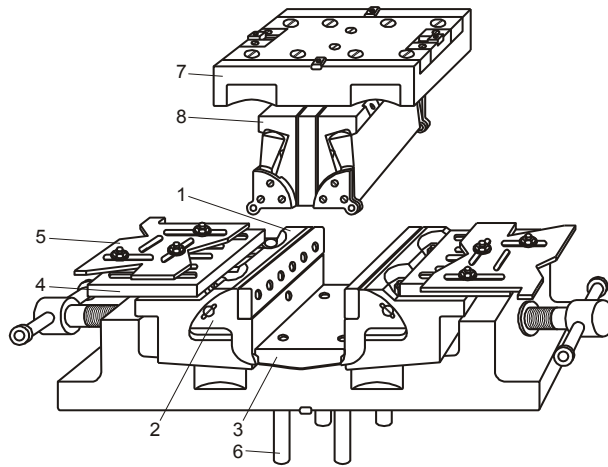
Змінний переналагоджуваний пакет для двохкутового згинання деталей із заданими параметрами точності
